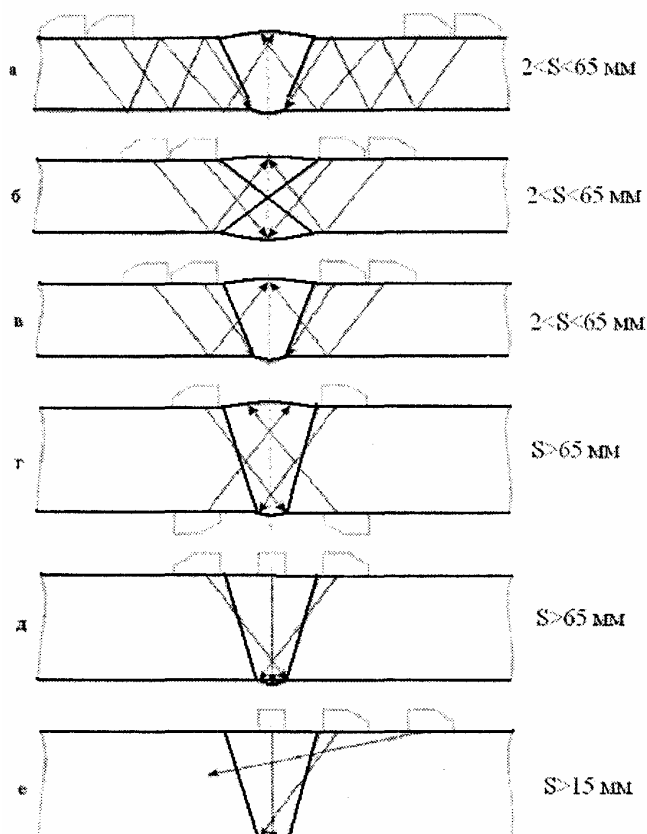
Рекомендованные схемы контроля для стыковых сварных соединений
